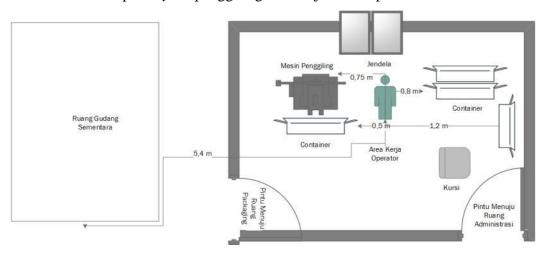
Layout Kerja Awalan Pengolahan Susu
